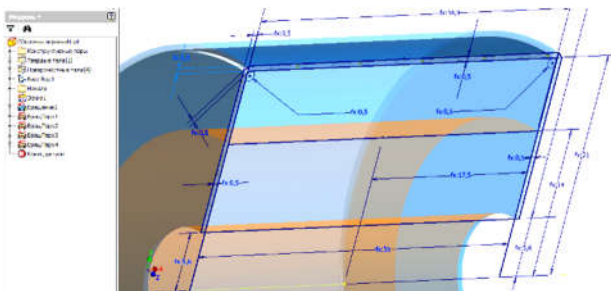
Побудова 3D-моделі "оболонка циліндричного черв'яка"
